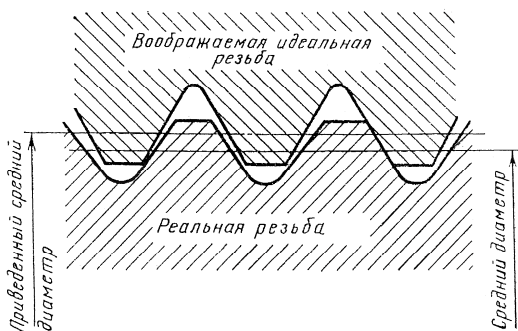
Приведенный средний диаметр цилиндрической резьбы
